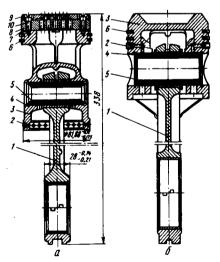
Шатунно-поршневые группы: а — компрессора АУ45; б — компрессора П80; 1 — шатун в сборе; 2 — кольцо маслосъемное; 3 — поршень; 4 — кольцо стопорное; 5 — палец; 6 — кольцо компрессионное; 7 — прокладка; 8 — клапан всасывающий в сборе; 9 — шайба замочная; 10 — винт
